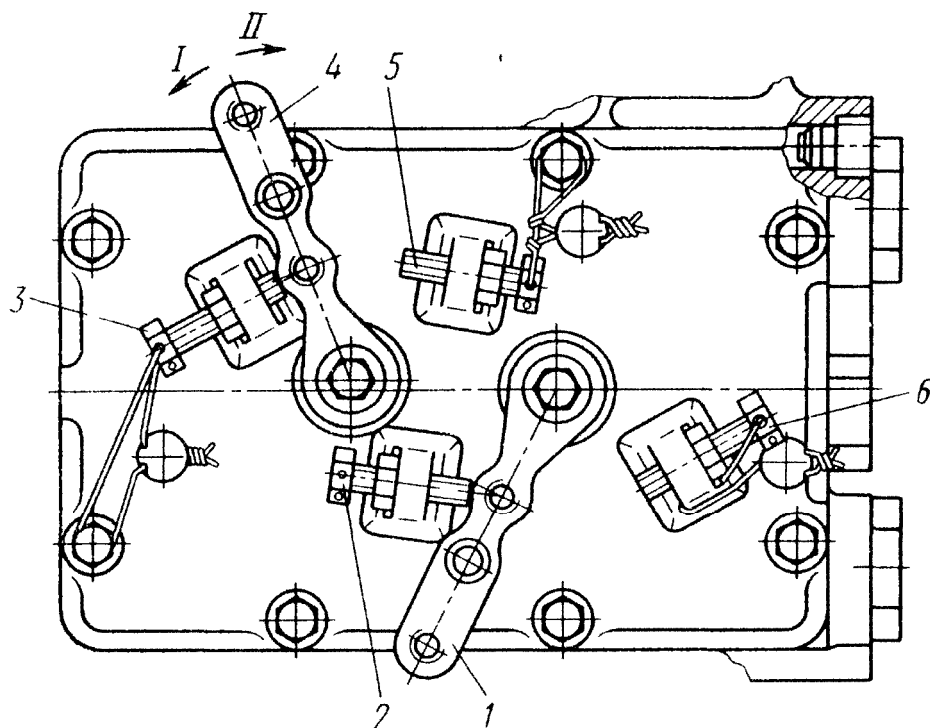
Крышка регулятора с рычагами подачи топлива и останова двигателя:
